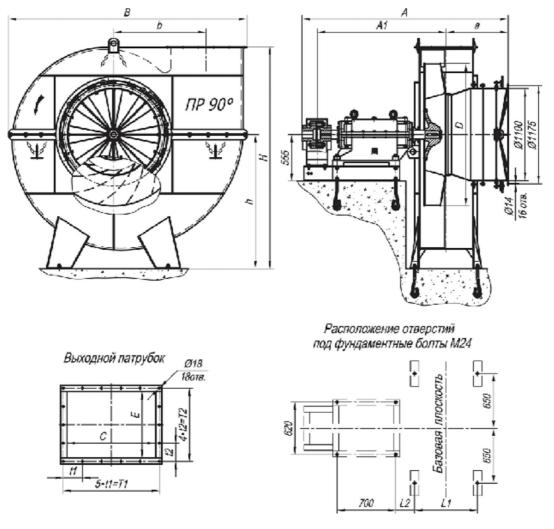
Габаритные и присоединительные размеры тягодутьевых машин типа ВДН и ДН №15 и №17 исп-3.
